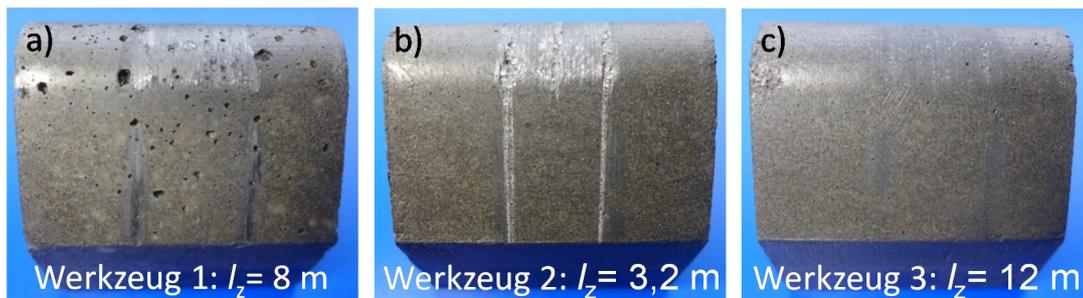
Endzustand der Werkzeuge nach Reinigung
